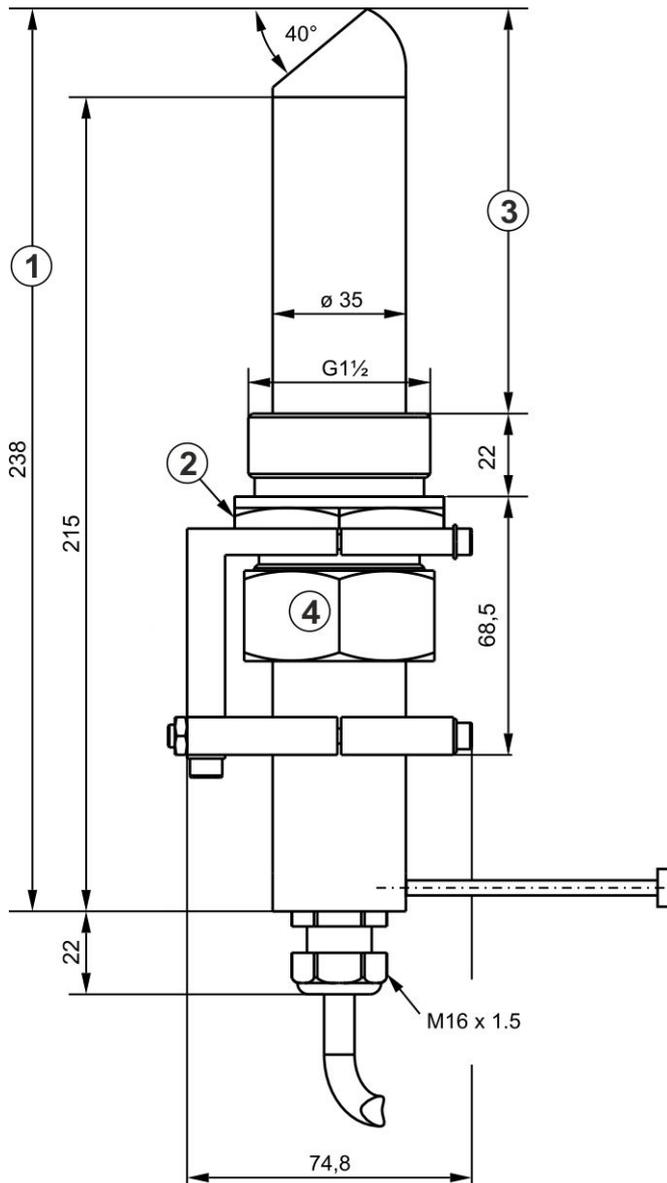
Maßzeichnung Keilsensor CS2-....K
